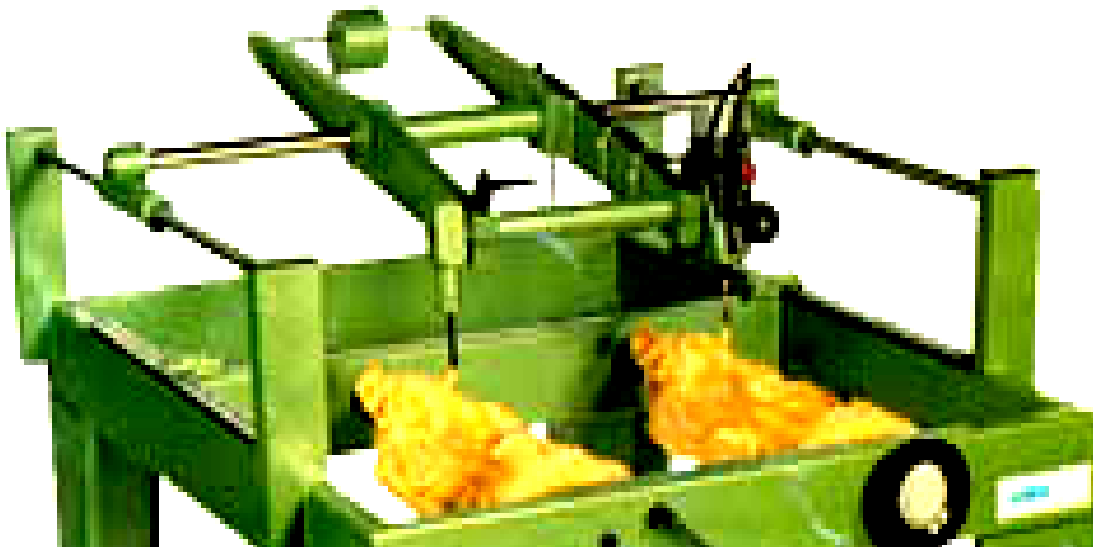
Фрезерний об'ємно-копіювальний пантограф [6].
